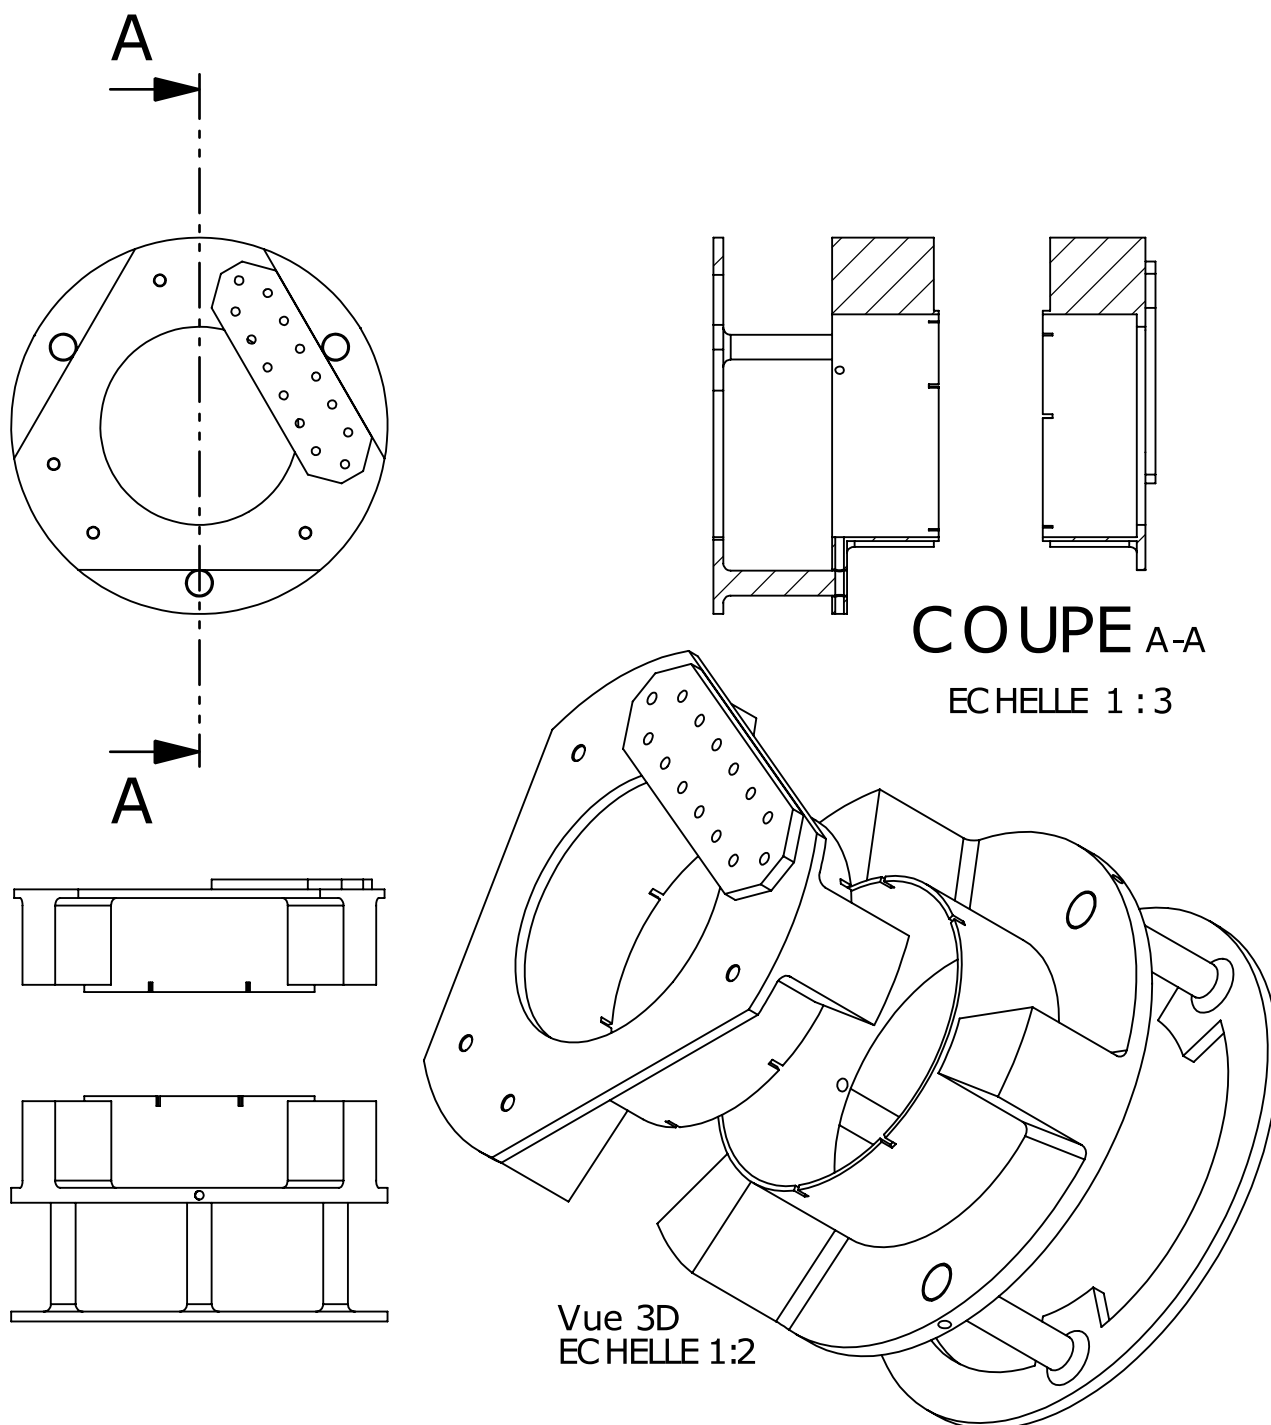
Dessin technique de l'assemblage des supports de mesure des stators
